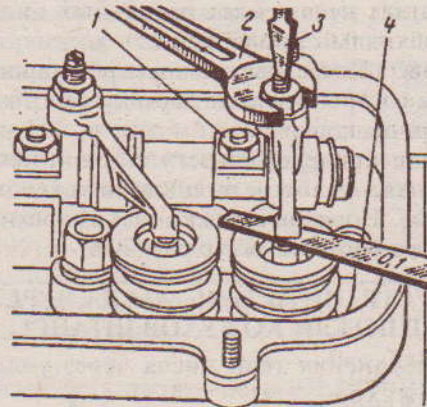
Регулировка тепловых зазоров в клапанном механизме: 1 - гайка; 2 - ключ; 3 - отвертка; 4 - щуп
